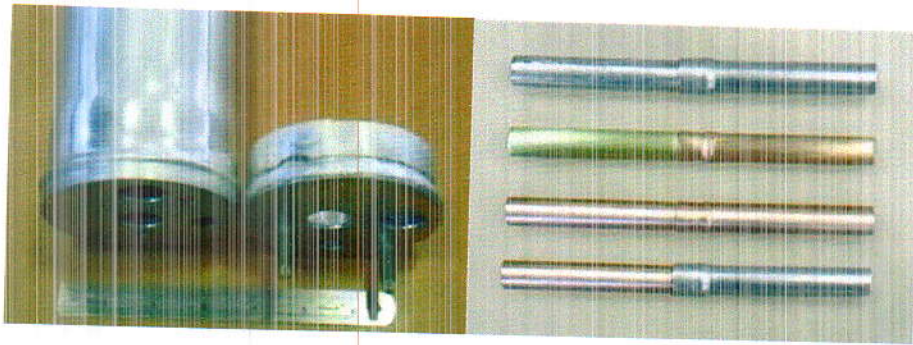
Pièces formées par Soudage électromagnétique
